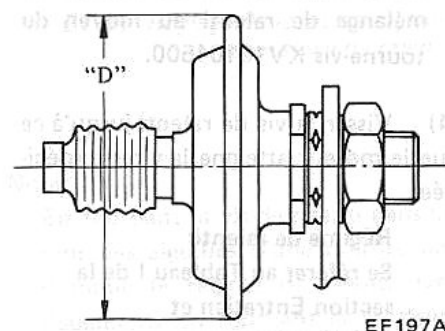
Dimension de "D" des soupapes d'amortissement
